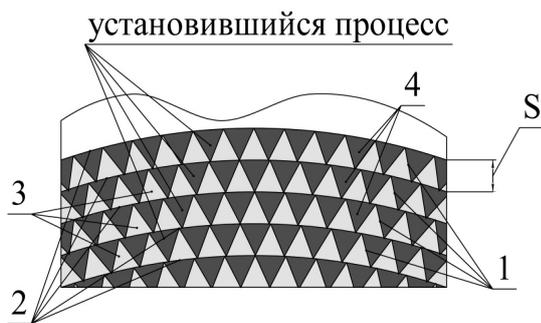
Формообразование порошка при ротационном фрезеровании: 1 – траектория движения зубчатой режущей чашки; 2 – траектория движения гладкой режущей чашки; 3 – порошок, срезаемый зубчатой режущей чашкой; 4 – порошок, срезаемый гладкой режущей чашкой
